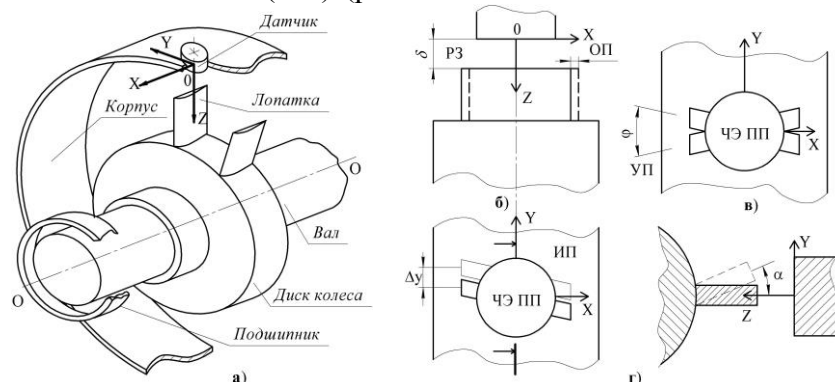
Элементы ротора лопаточной ЭУ, развёртка лопаточного венца с угловыми и линейными перемещениями лопаток
